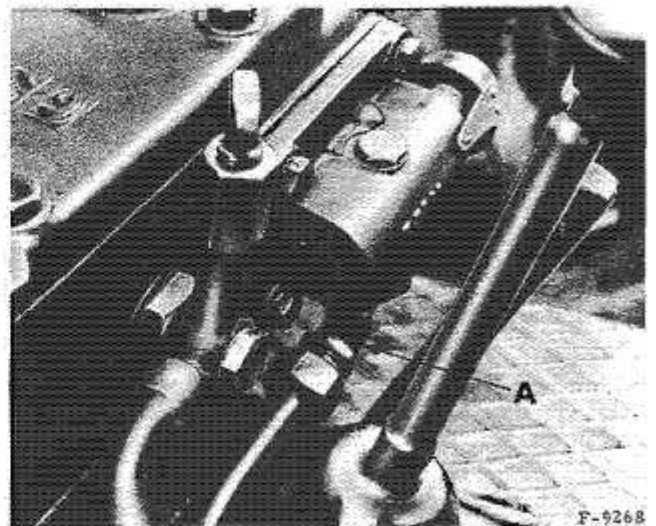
Assemblage tuyauterie - raccord coudé.
